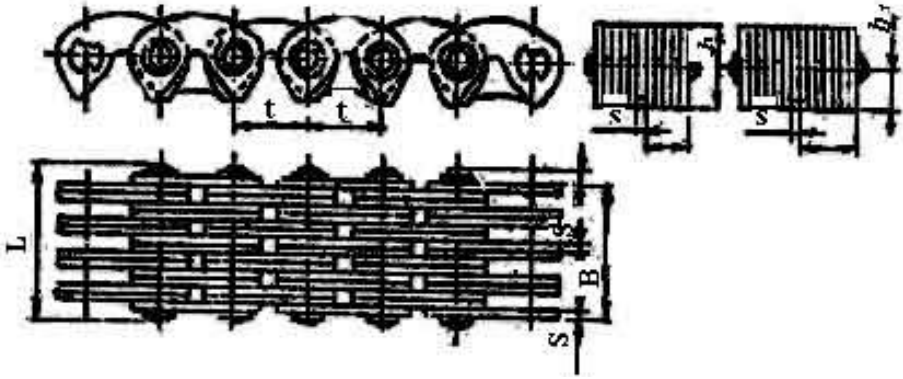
Зубчатий ланцюг з шарнірами кочення за ГОСТ 13552-68
